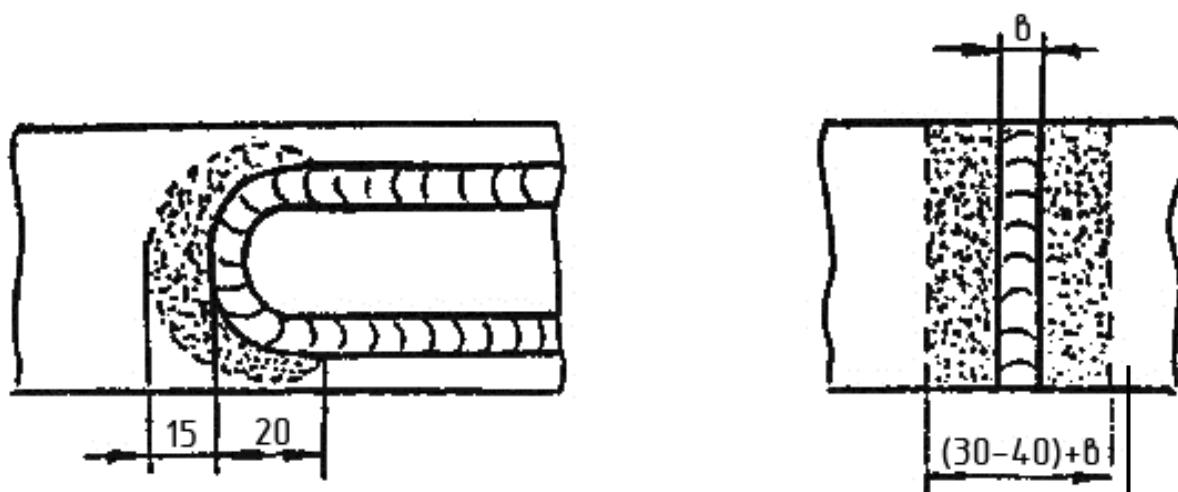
Места наклепа сварных соединений
